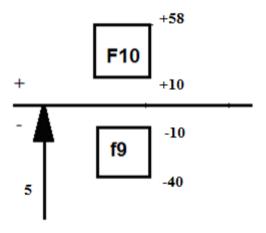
Схема полей допусков шлицевого соединения
